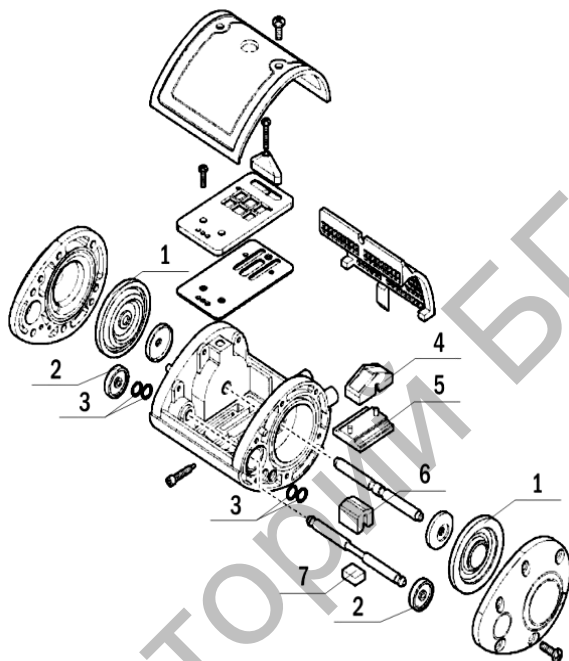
Схема и общий вид гидравлического пульсатора парного доения:
